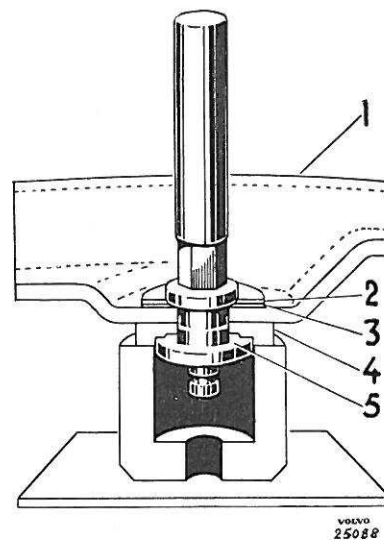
Démontage du boulon (segment arrière de roue arrière).
